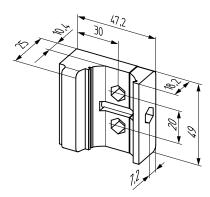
Croquis de dimensiones del soporte QuickFix (2066048)
